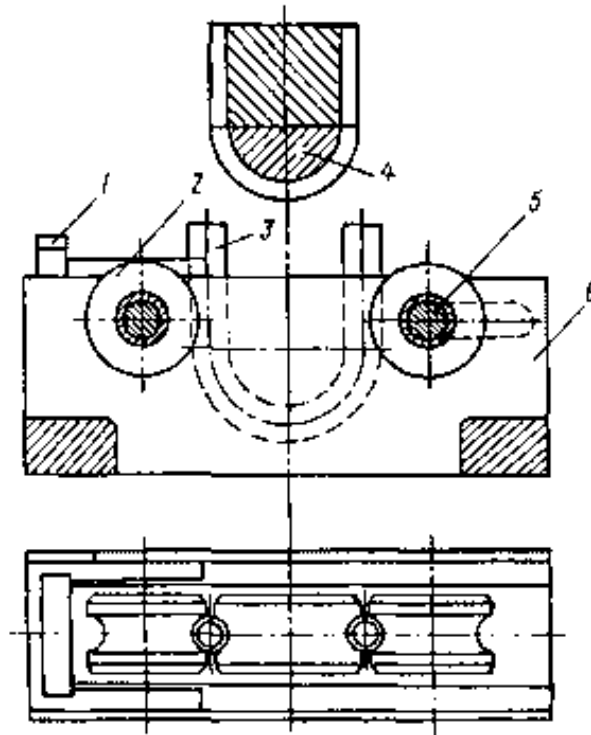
Схема штампа для згинання колін з прямими ділянками
